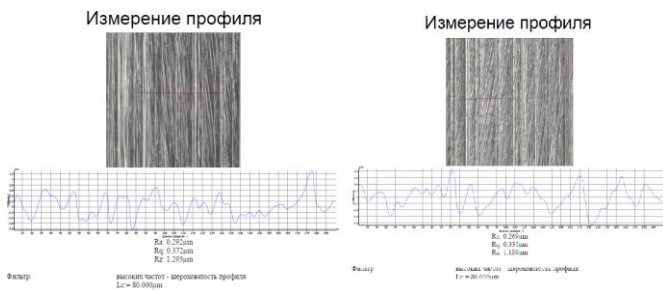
Шероховатость поверхности детали при зубохонинговании с помощью шевира
